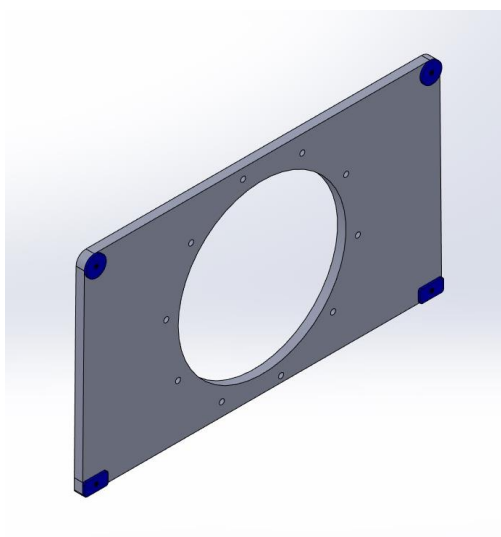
Conjunto Placa Traseira e Patelas a Soldar no Quadro
